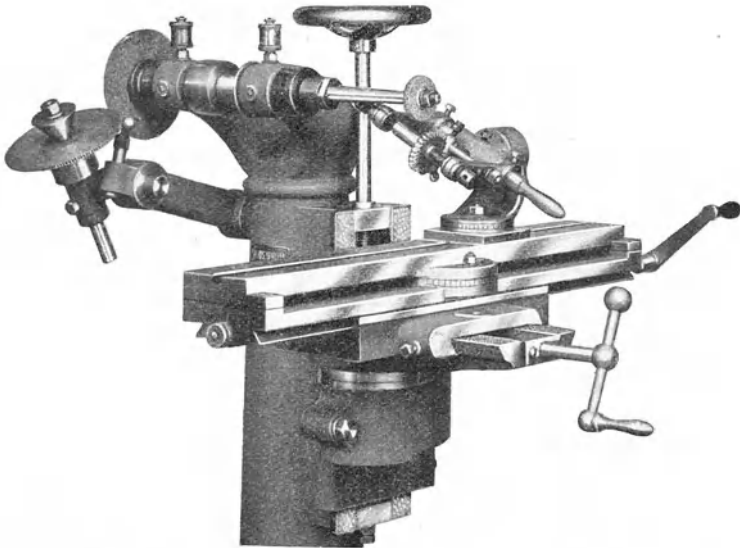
Das Schärfen eines gerieften Profilfräasers mit dem Drehteil des Universalböckchens.
